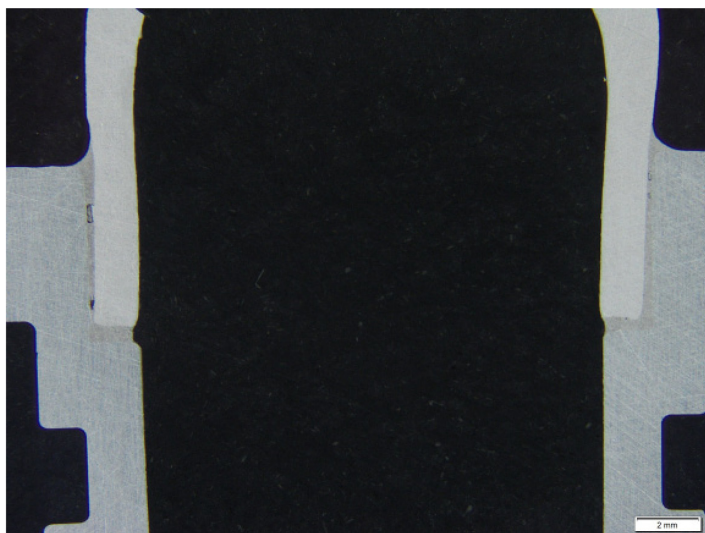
Makrostruktura pájeného spoje držáku řezem u zkoušky č.6 Zv.10x
